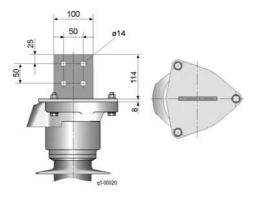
Conexión de alta tensión con terminal plano (DIN)
